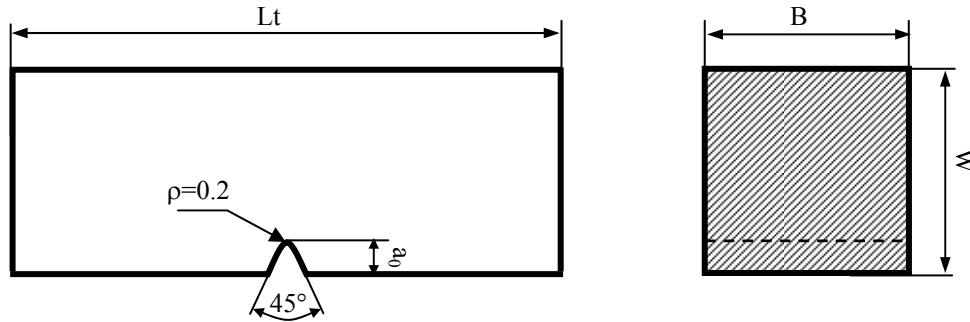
Géométrie des éprouvettes de fissuration
